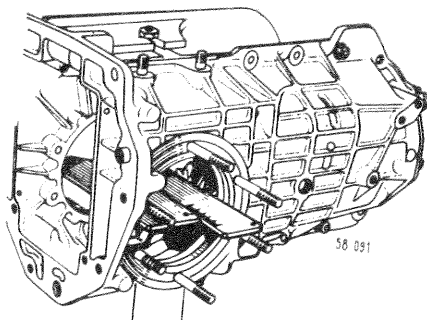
Mise en place de la règle graduée pour réglage de la distance conique
